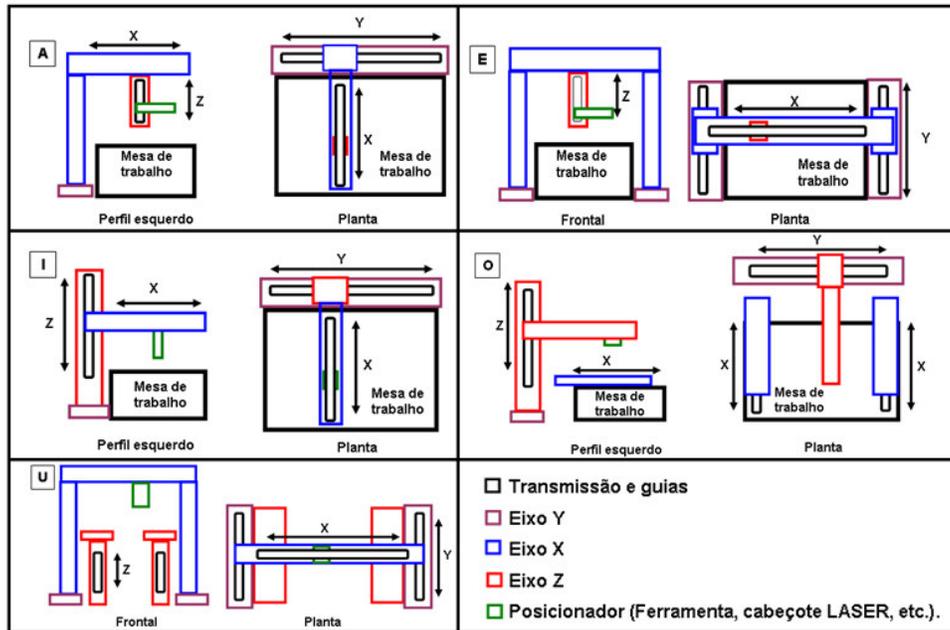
Concepções de estruturas para a máquina. Fonte: Autor
